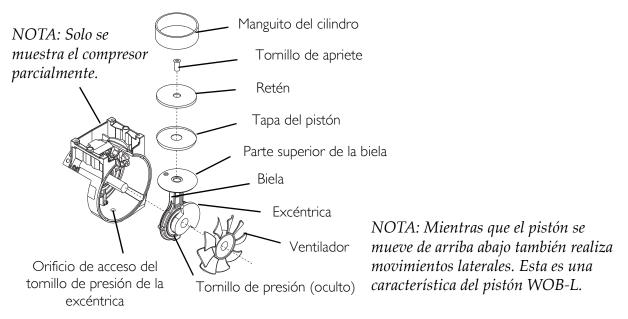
Retirada del compresor y de las cubiertas del compresor - Reconstrucción del compresor - Ventilador - Conexión del conjunto de la excéntrica y la biela - Tapa del pistón
